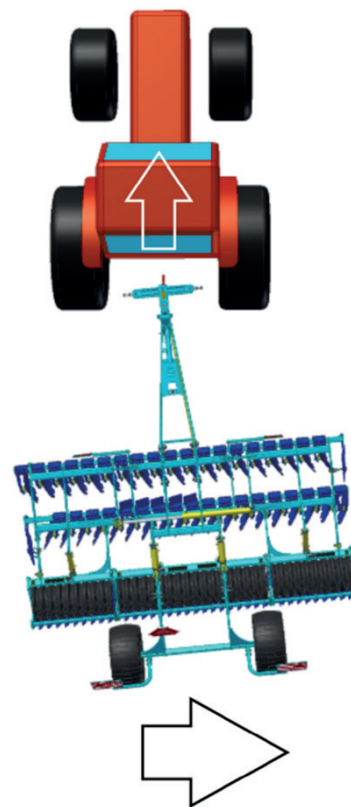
Схематическое изображение «дрейфа» дискового луцильника Farmet Softfer 6 PS с классической схемой расстановки рабочих органов
